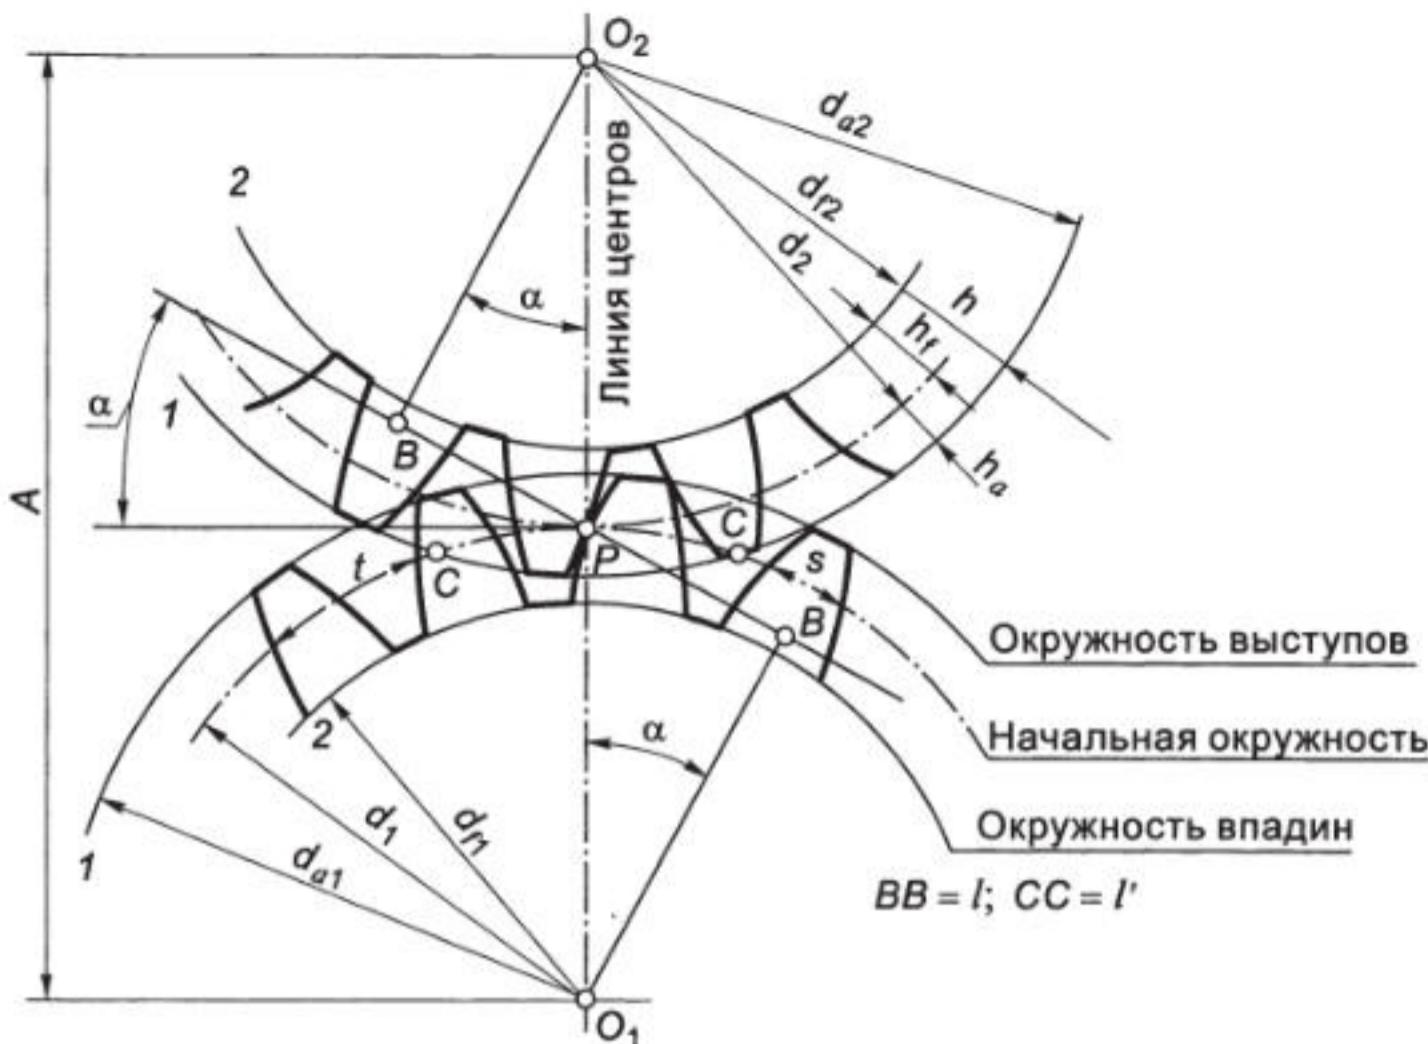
Параметры эвольвентной зубчатой передачи
